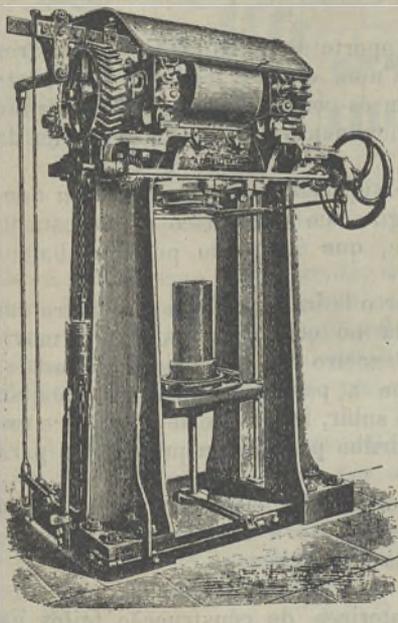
Machina para fabricar manilhas, com cylindros compressores
